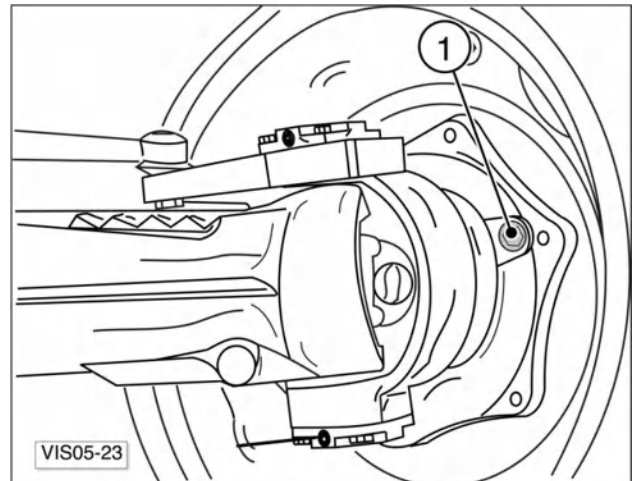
Передний колесный редуктор: (1) заливная, контрольная и сливная пробка.
